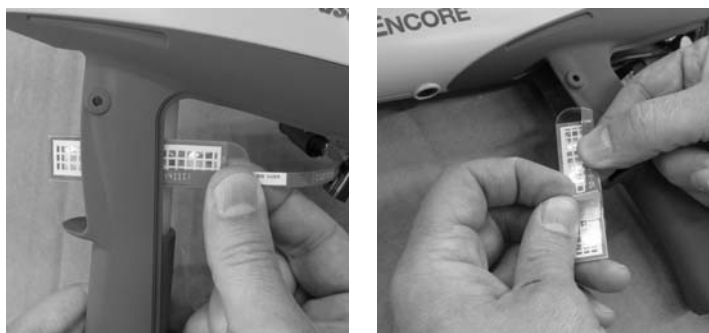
Установка выключателя спускового устройства — операции 1 и 2
